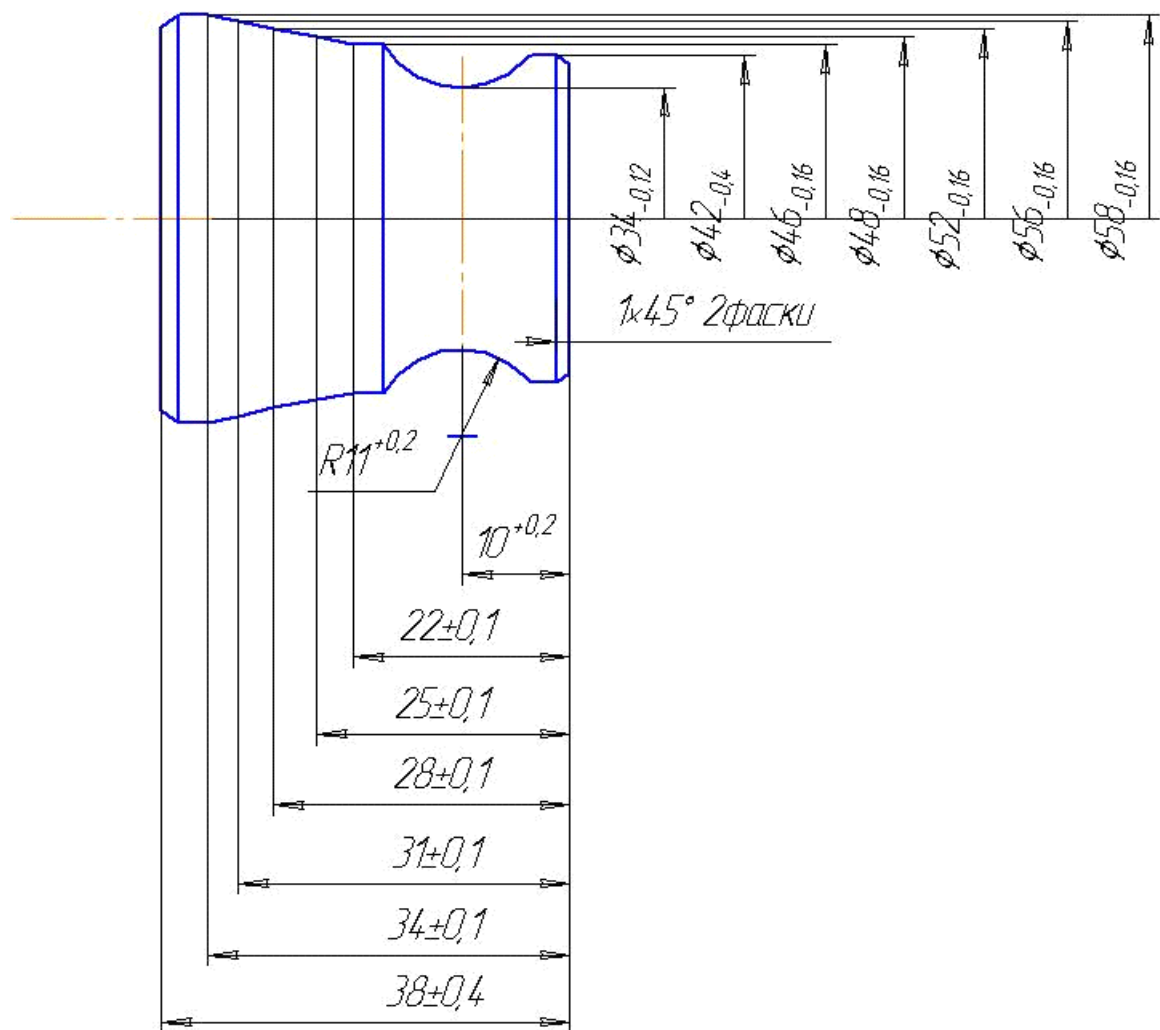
Деталь, обрабатываемая фасонным резцом
